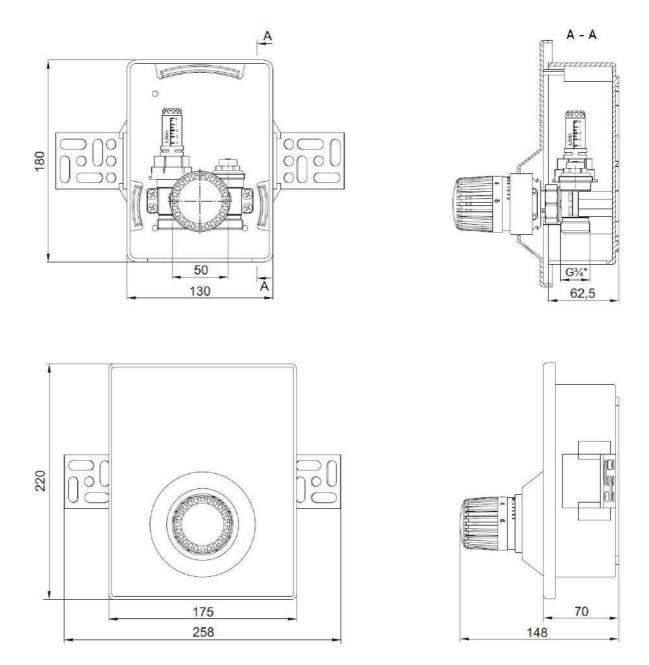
Габаритные размеры регулировочного короба Oks00731
